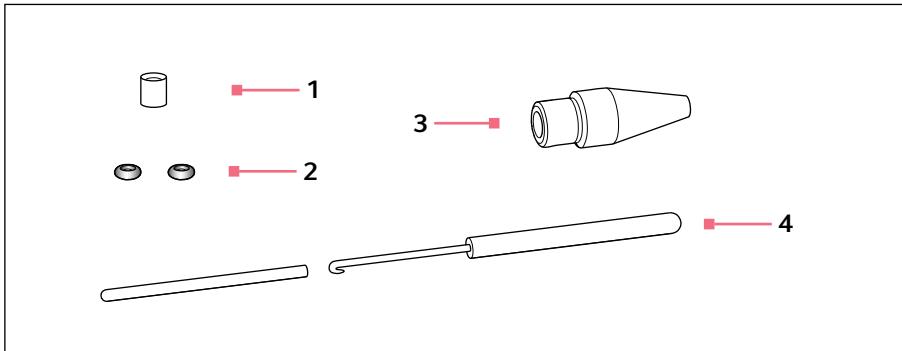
Spannkopf 4 mit Entnahmewerkzeug
